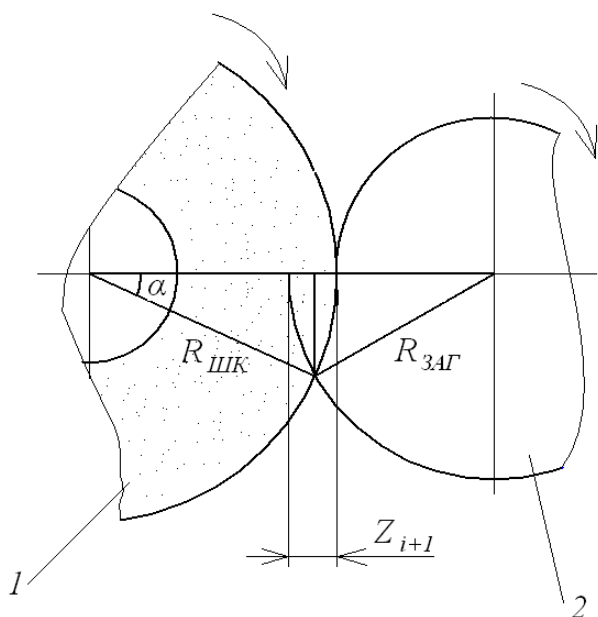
Схема круглого наружного шлифования: 1 – шлифовальный круг; 2 – обрабатываемая заготовка; α – угол контакта круга с заготовкой, град.
